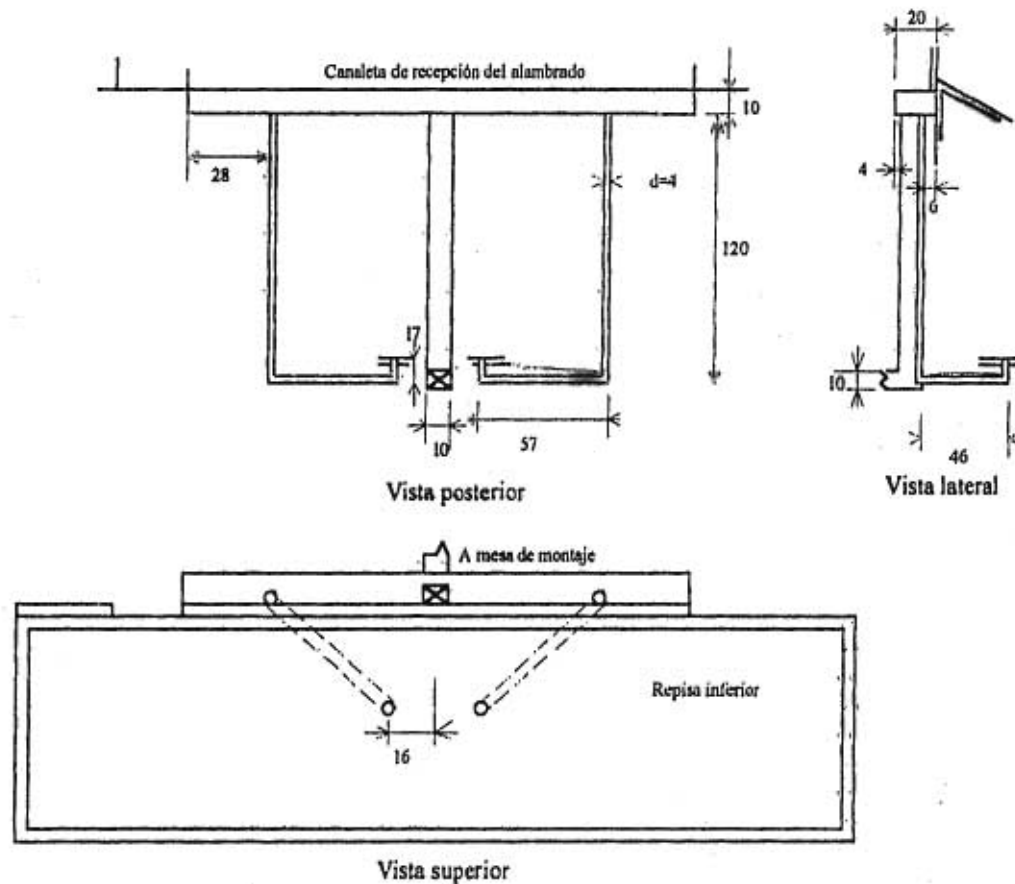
Detalle de la acometida a repisa inferior y a mesa de montaje.
